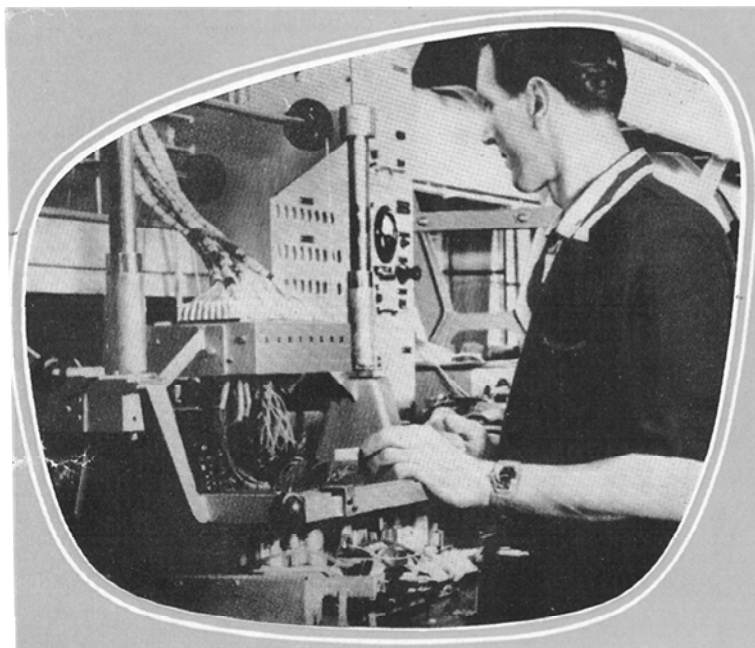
Komplettprüfung des Chassis am „Sturen Otto“
